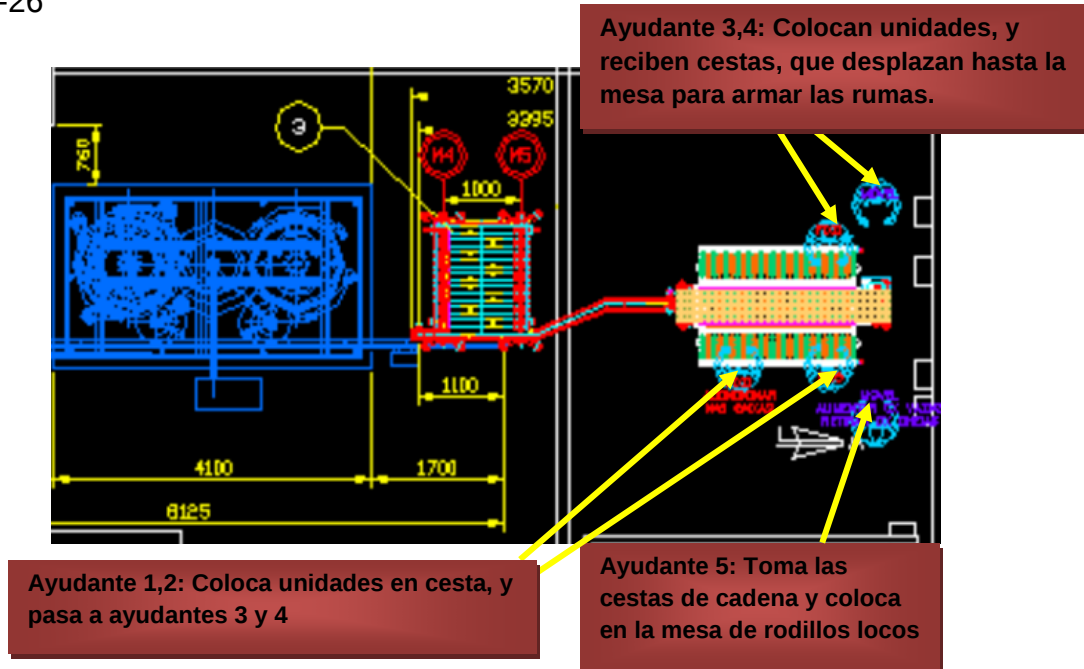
Distribución en planta de máquina envasadora Serac DT-26. Ayudantes
